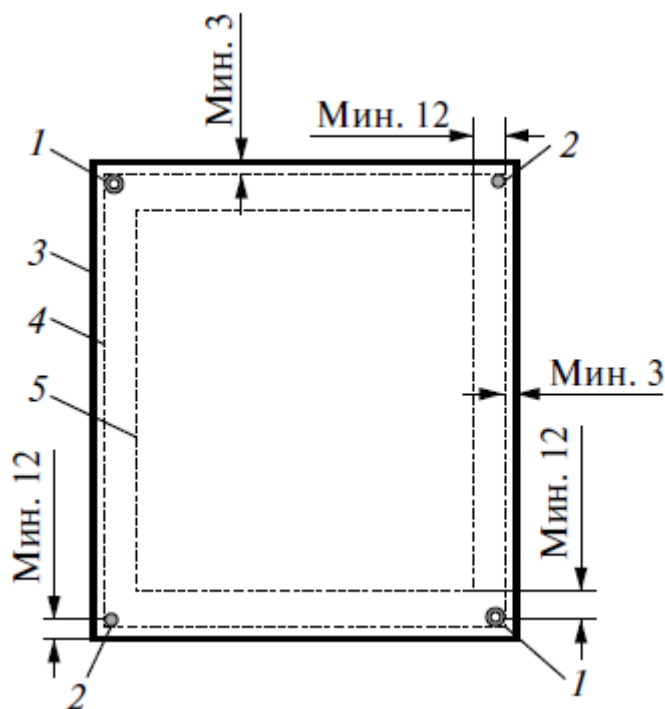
Размещение реперных знаков на заготовке ПП: 1 – базовые отверстия; 2 – реперные знаки; 3 – периметр заготовки ПП; 4 – периметр мультиплицированной заготовки (панели), поступающей на сборку; 5 – рабочее поле заготовки, на котором размещаются платы
